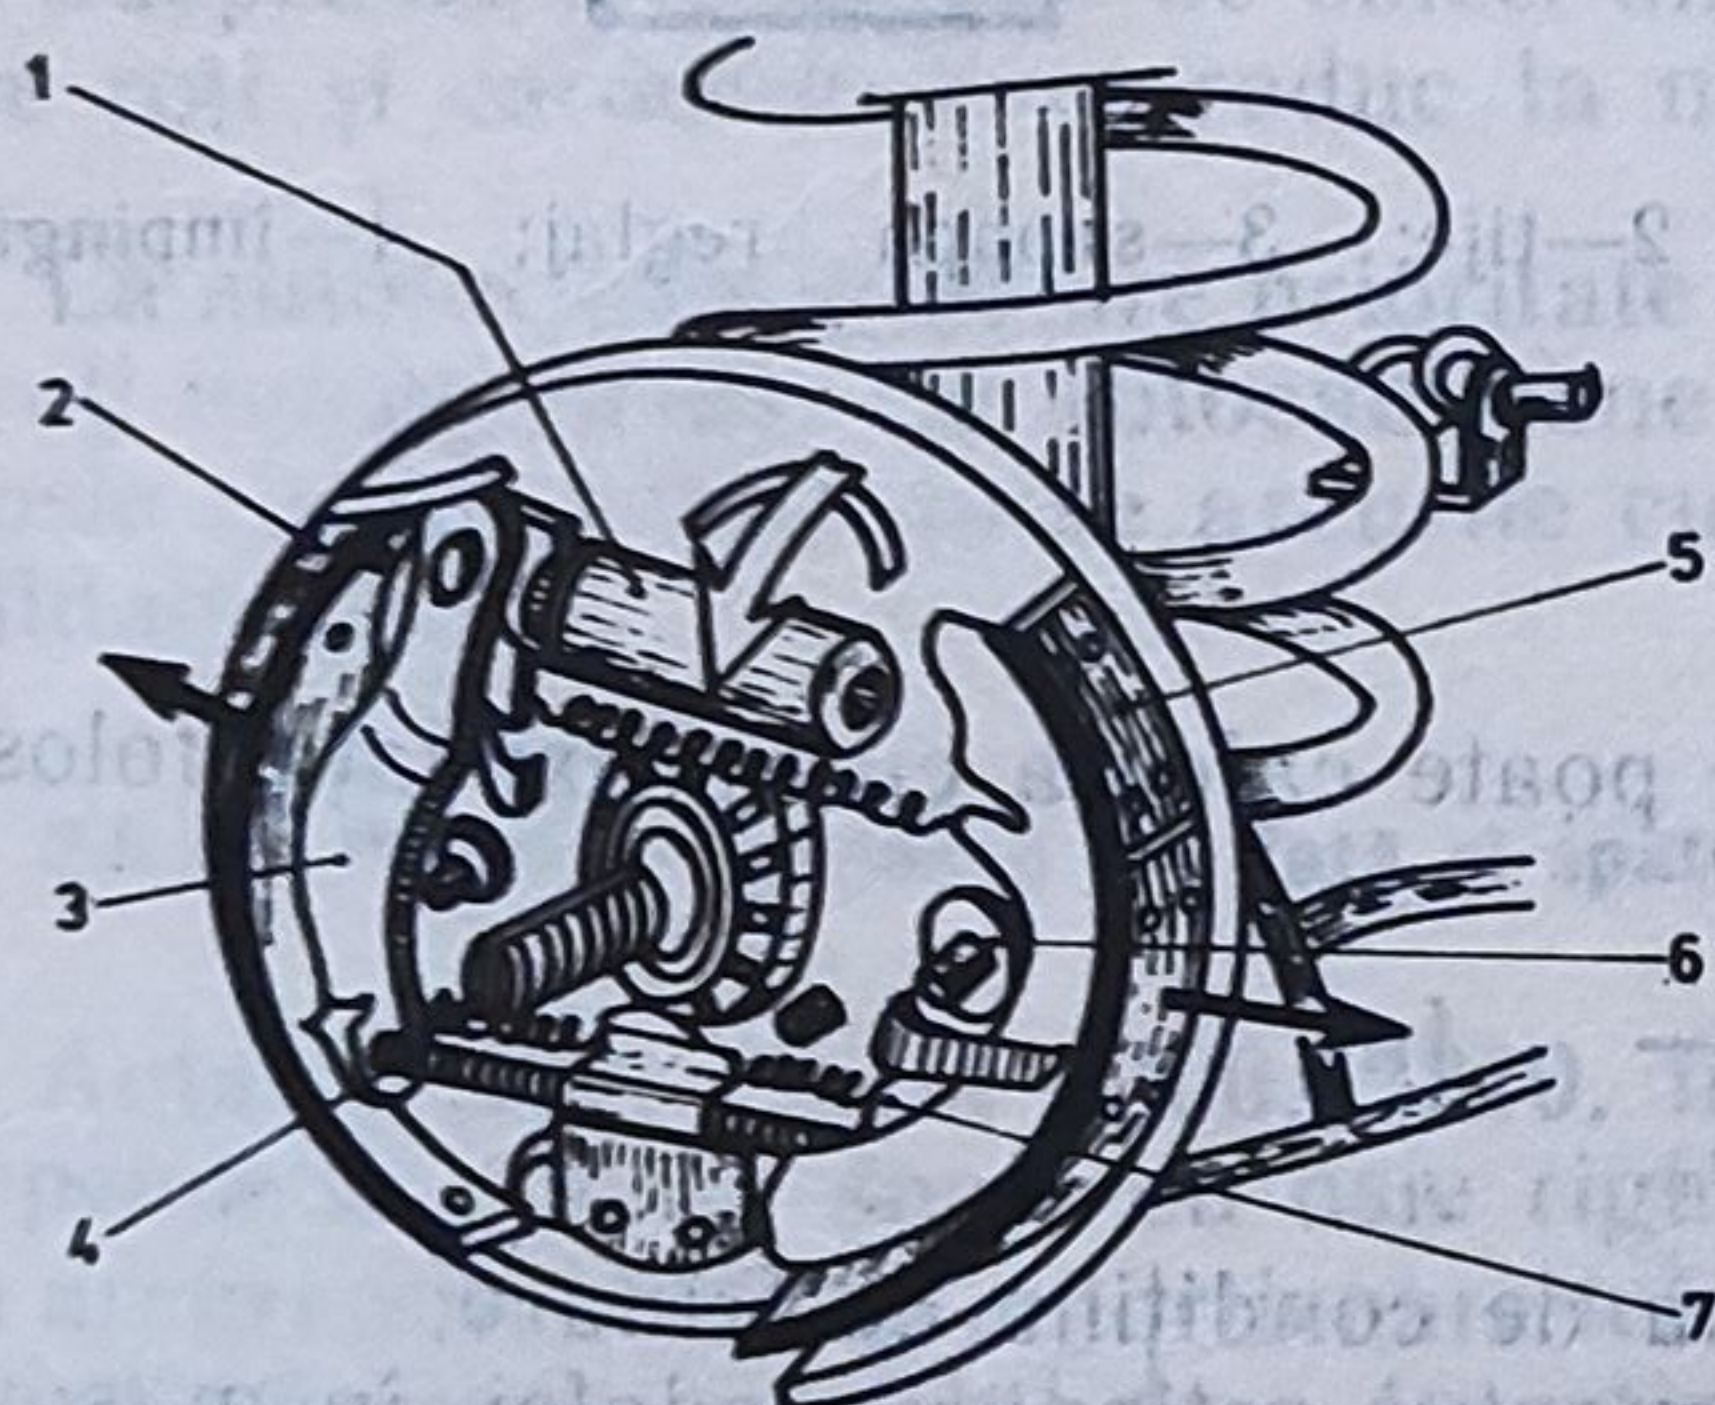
35a a. Frînă cu tambur la roțile din spate ale autoturismului Dacia 1300: 1—cilindrul receptor; 2—sabot de întindere; 3—levier de acționare a frinei de mînă; 4—arcuri de readucere; 5—sabot de compresiune; 6—excentric pentru reglarea jocului între saboți; 7—cablu
